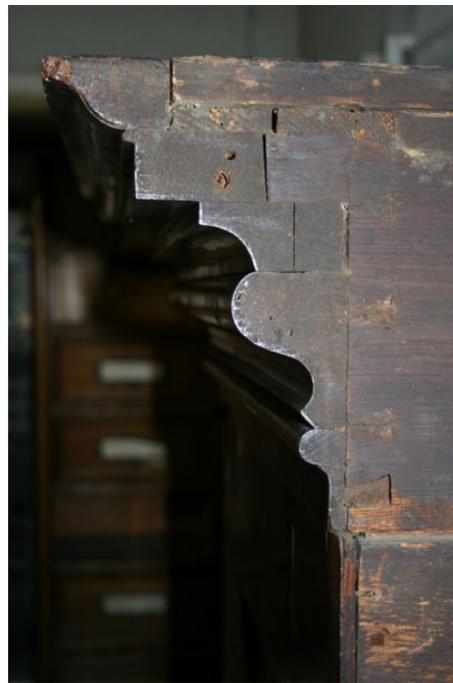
Kastenkonstruktion Gesims mit umlaufender Profilierung
